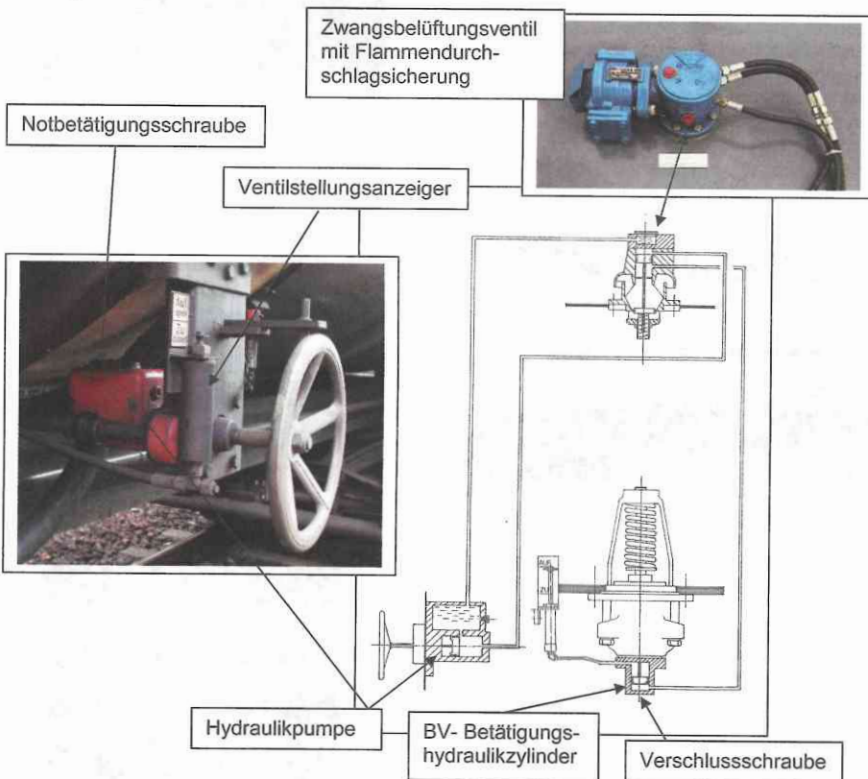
hydraulisch betätigtes BV mit Zwangsbelüftung
